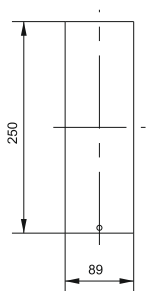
Заглушка приборная ONFLOOR / Figure 5 – Instrument end plug ONFLOOR / 5-suret – ONFLOOR aspartıyq biteuşı / Рисунок 5 – Заглушка приладова ONFLOOR
